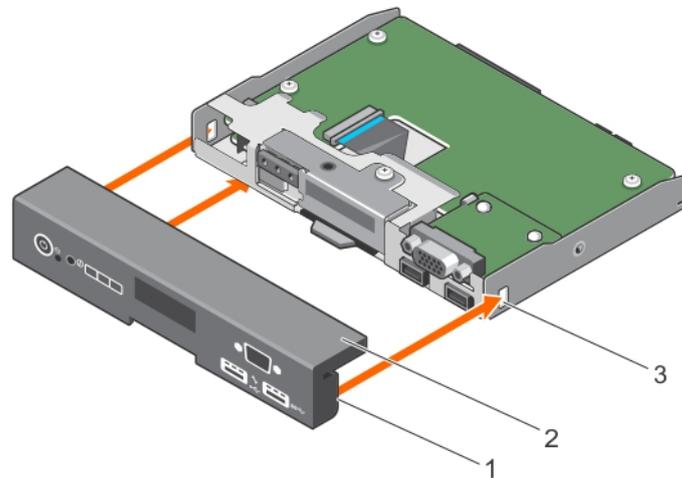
Instalación de la cubierta del ensamblaje del panel de control para un sistema con panel LCD.
